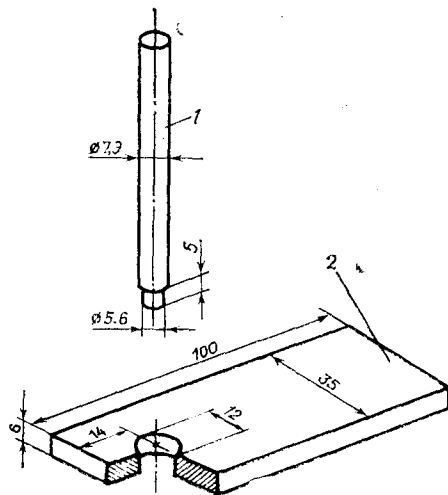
Приспособление для выпрессовки втулки Ш6500-204 в вилках тяг управления двигателем:
